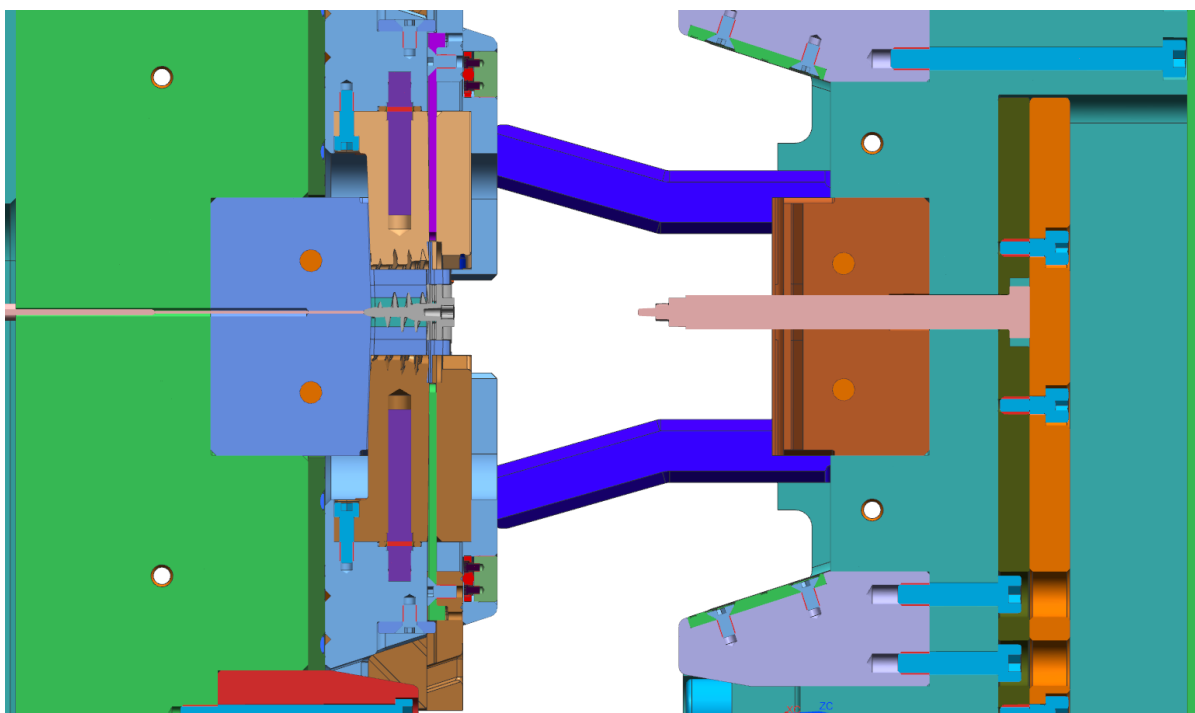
Vedení vyhazovacích desek od firmy meusbarger
